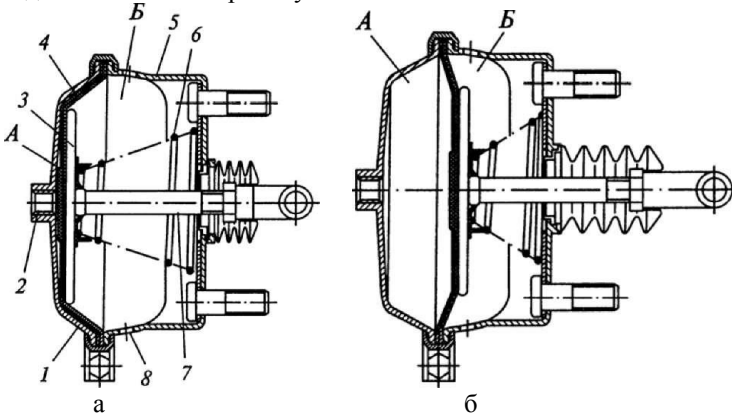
Гальмівна камера у розгальмованому стані (а) і при гальмуванні (б): 1 - кришка; 2 - штуцер; 3 - диск; 4 - діафрагма; 5 - корпус; 6 - пружина; 7 - шток; 8 - отвір; А,Б – порожнини.
